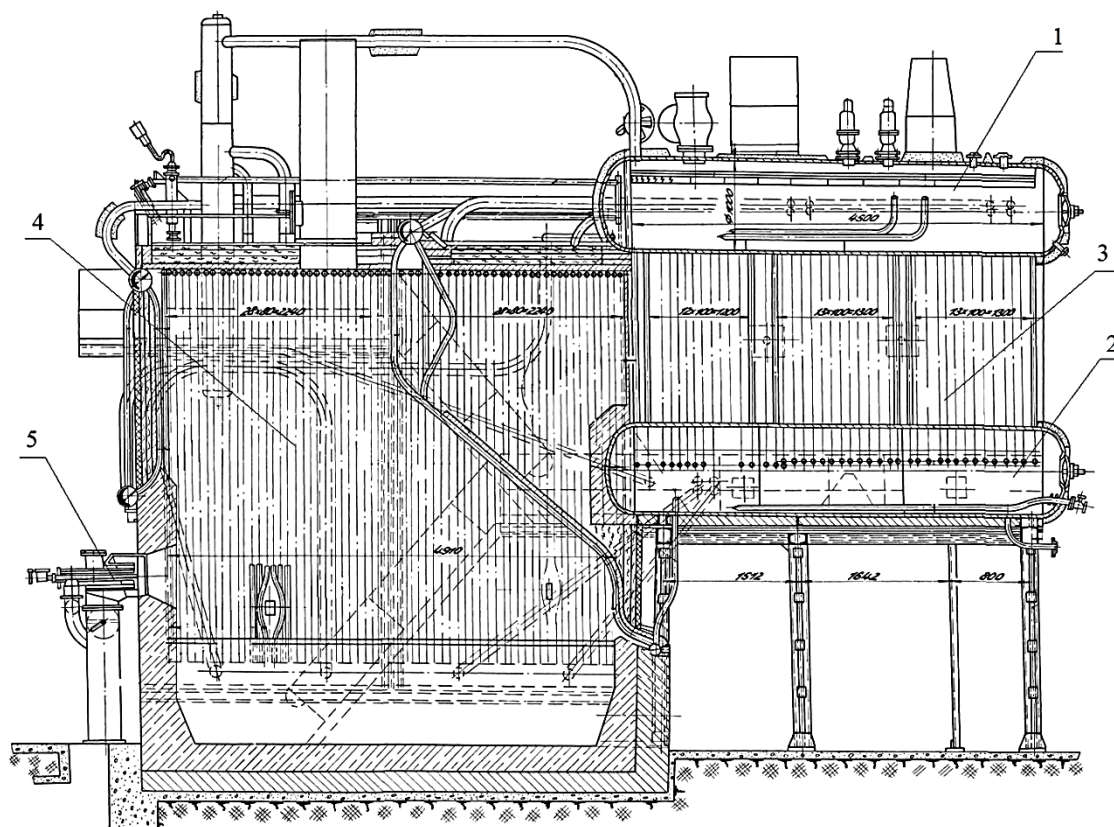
Котел ДВКР-20 ГМ: 1 и 2–верхний и нижний барабаны соответственно; 3–котельный пучок; 4–экранные поверхности топочной камеры; 5–горелка газомазутная.
